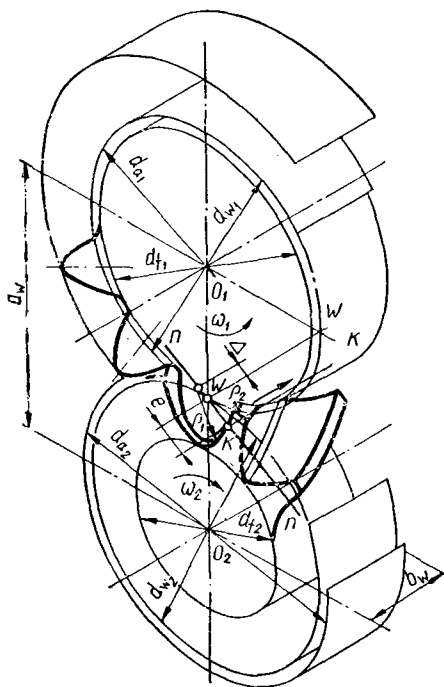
Зубчатый механизм с одной линией зацепления
